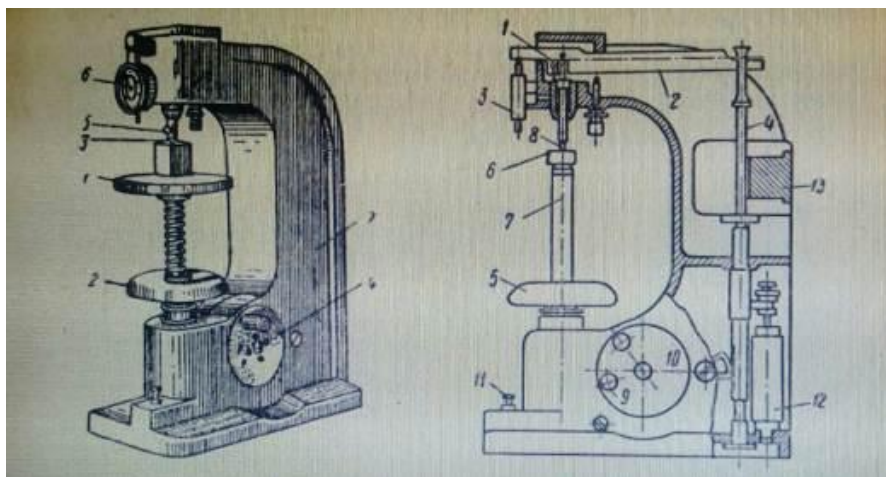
А-прибор Роквелла: 1-подставка, 2-маховик,3-алмазный конус, 4-рукоятка, 5-наконечник, 6-индикатор,7-станина;
